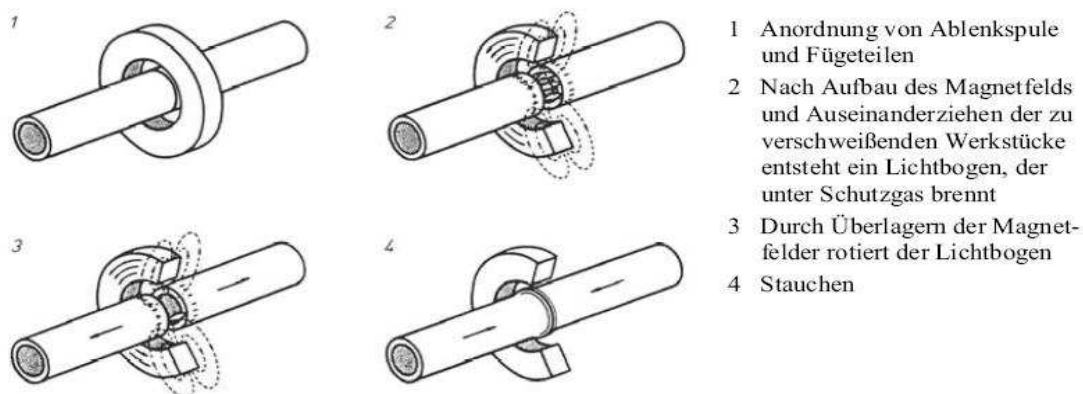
Schematische Anordnung beim MBL-Schweißen<sup>[ST02]</sup>
